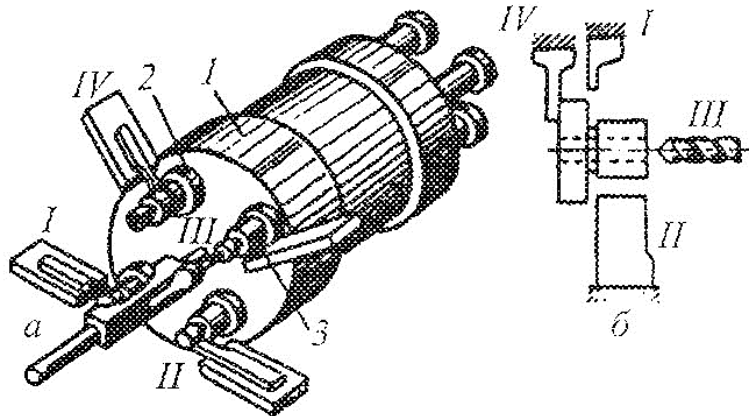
Схема обробки заготовок на багатшпindelному автоматі
